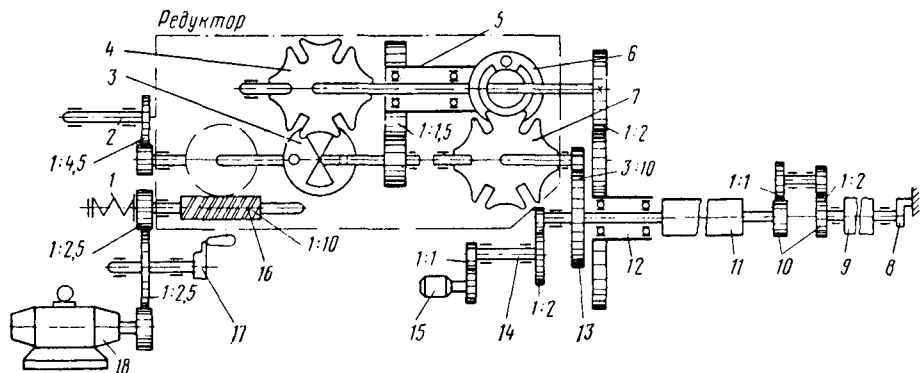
Кинематическая схема привода контроллера ЭКГ-8
